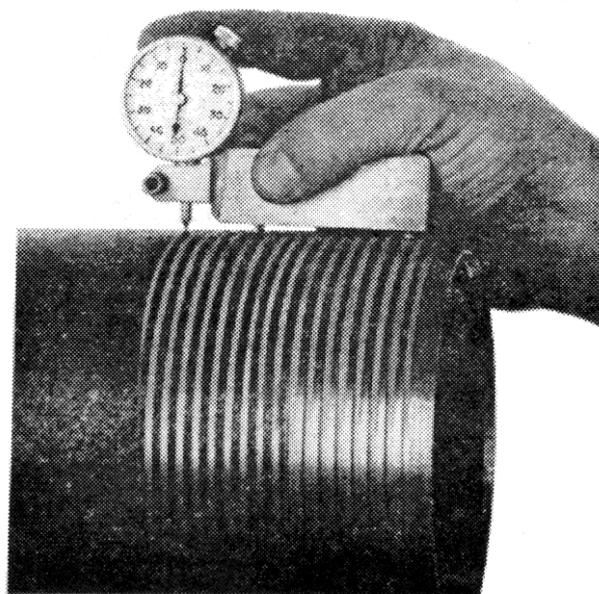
Типичный прибор для измерения сбега резьбы батресс обсадных труб
